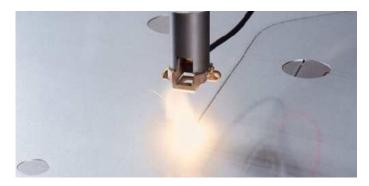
Proceso de Soldadura Laser para la Producción de TWB Fuente: TKS; Reaching Goals Together; 2008
